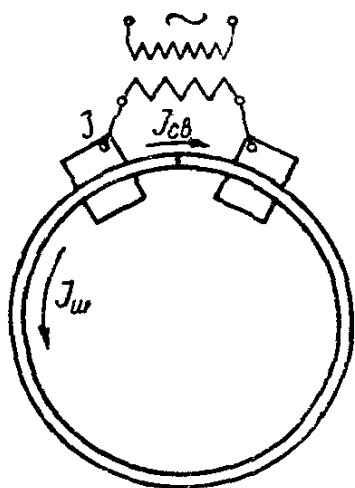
Кулачок для сварки непрерывным оплавлением.
